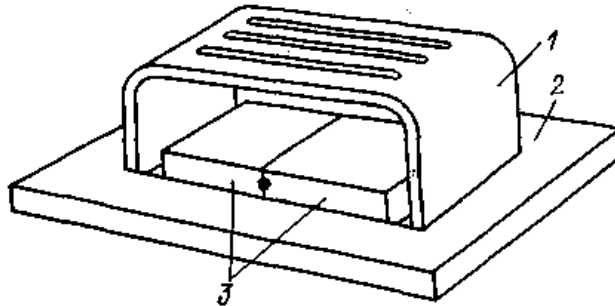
Размещение пробы в шаблоне для подводной сварки:
